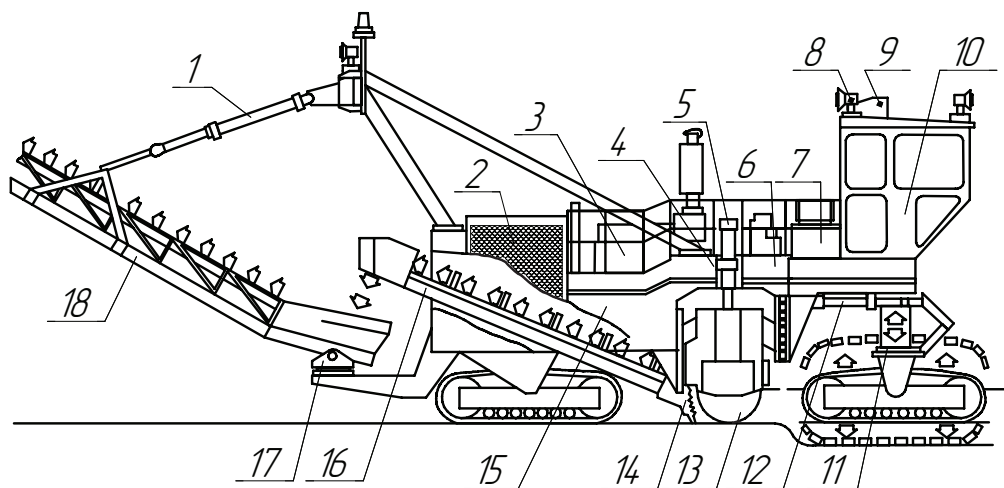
Схема фрезерного экскаватора Wirtgen:
